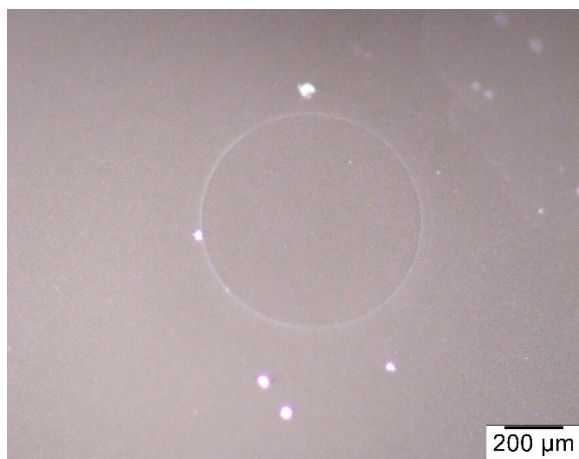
Aufnahme eines Ringrisses an einer Si_3N_4 -Kugel bei einem Kugel-Kugel-Kontakt (Draufsicht)
